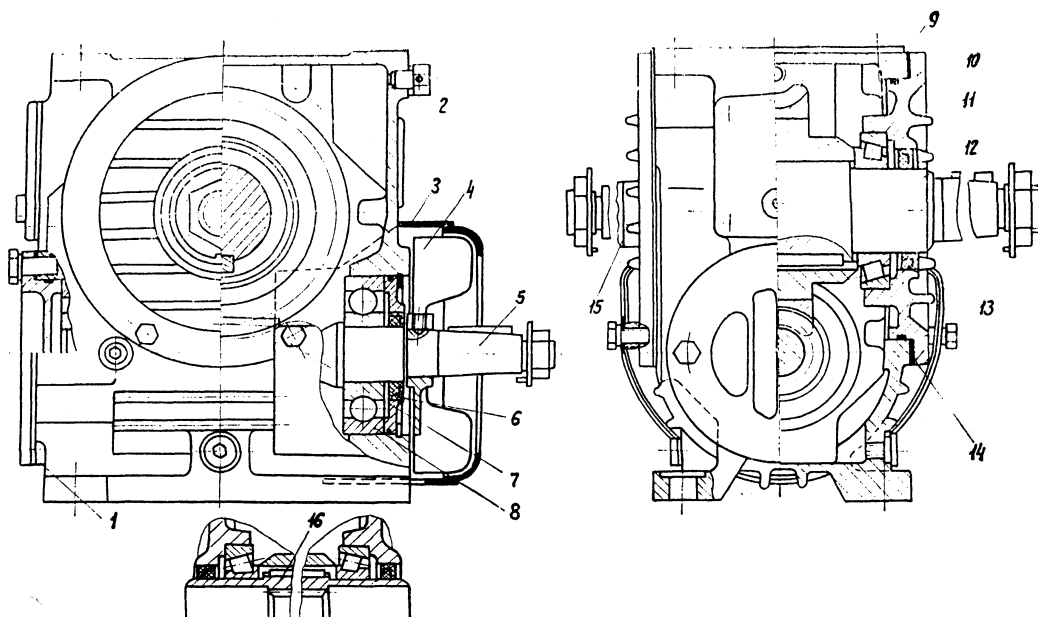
П7 Общий вид редукторов типоразмеров Ч-100, Ч-125, Ч-160
